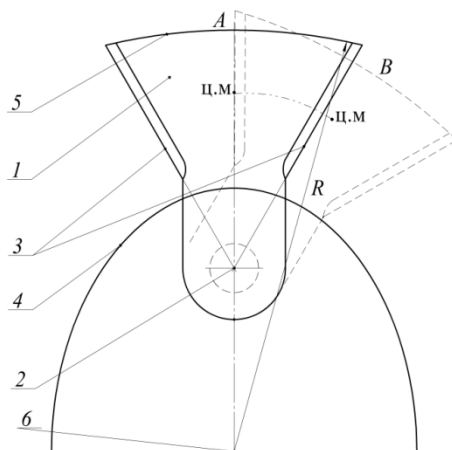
Конструкция трапецевидного ножа роторной косилки: 1 – нож; 2 – отверстие; 3 – режущие кромки; 4 – ротор; 5 – внешняя торцовая кромка; 6 – центр ротора
